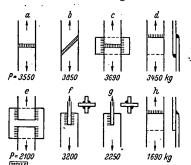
Festigkeit von Schweißverbindungen. Al-Cu-Mg ausgehärtet; Autogenschweißung; Blechdicke 3 mm Buchstabenerklärung s. Text
